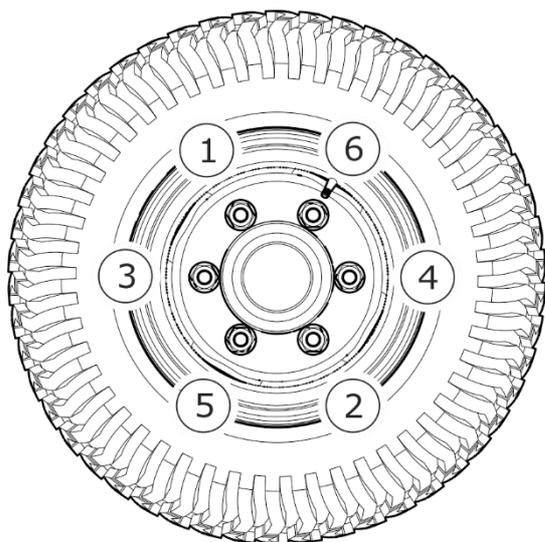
Ordre de desserrage et de serrage des écrous
